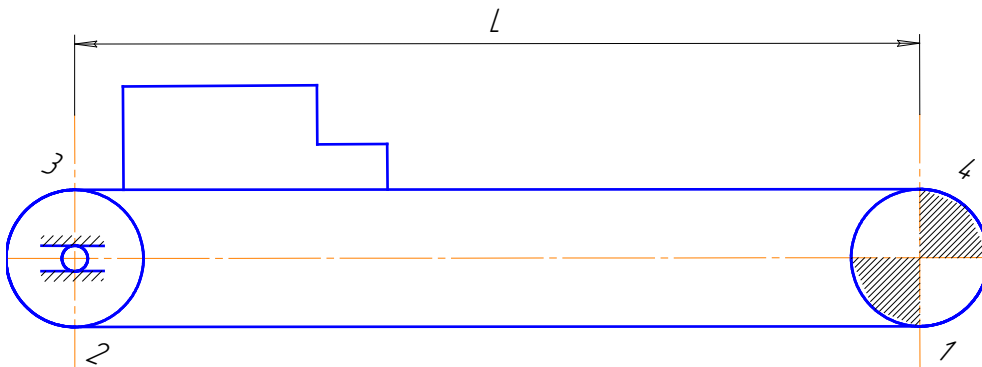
Розрахункова схема стрічкового конвеєра
